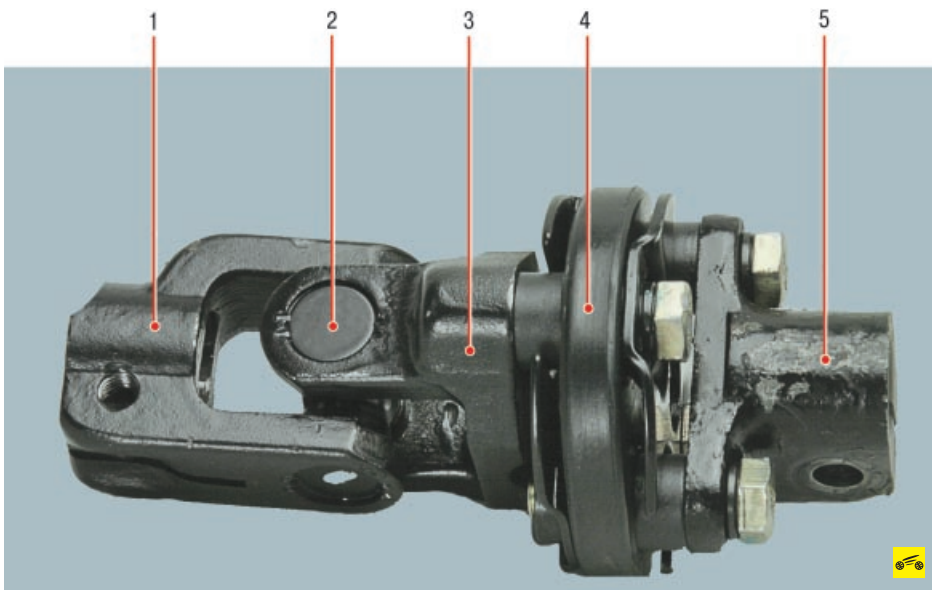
Верхний карданный шарнир промежуточного рулевого вала: 1 – верхняя вилка; 2 – крестовина; 3 – нижняя вилка; 4 – энергопоглощающий демпфер; 5 – фланец вала рулевого механизма
